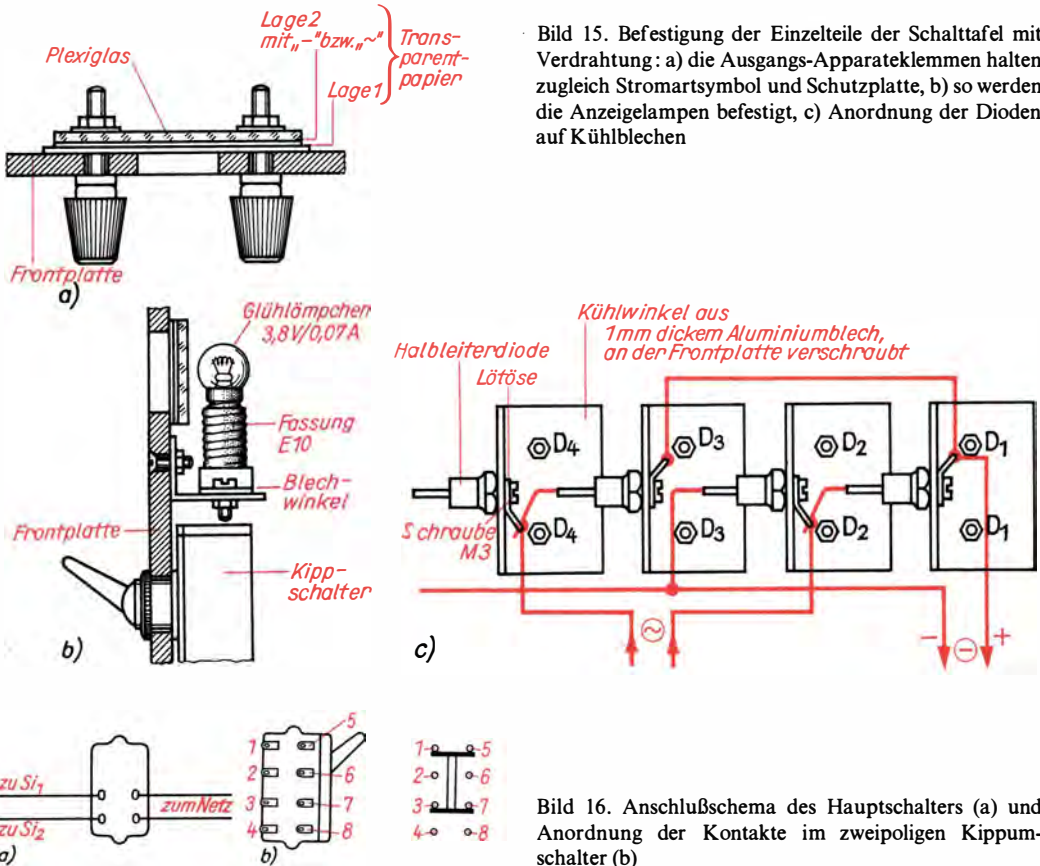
Befestigung der Einzelteile der Schalttafel mit Verdrahtung: a) die Ausgangs-Apparateklammern halten zugleich Stromartsymbol und Schutzplatte, b) so werden die Anzeigelampen befestigt, c) Anordnung der Dioden auf Kühlblechen
